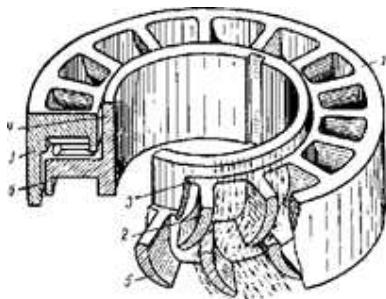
Общий вид статора и ротора турбобура и принцип действия турбины: 1 — наружное кольцо статора; 2 — лопатки статора; 3 — внутренний обод статора; 4 — внутреннее кольцо ротора; 5 — лопатки ротора; 6 — наружный обод ротора
